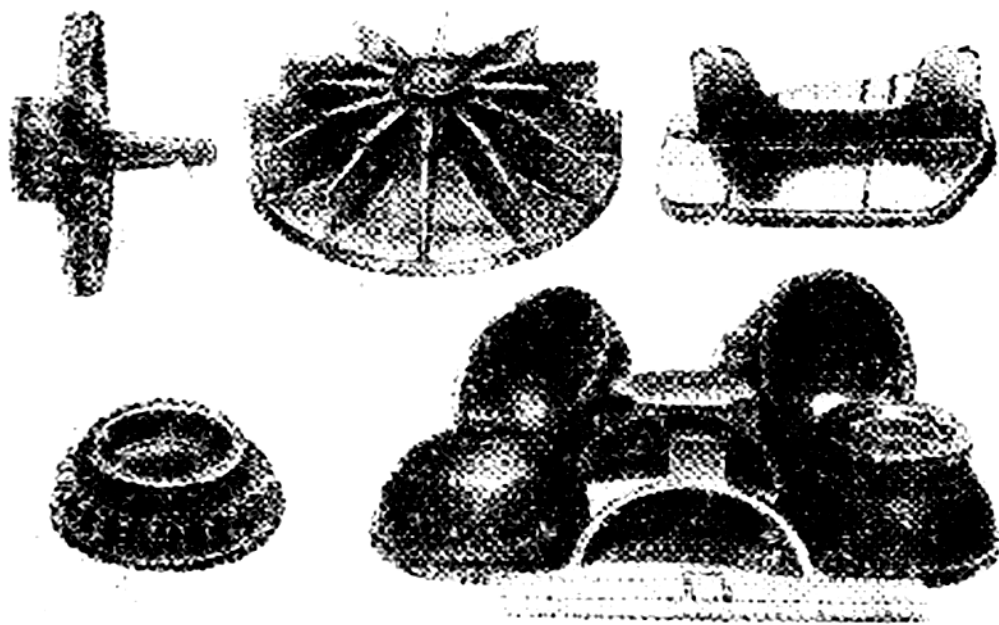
Типовые заготовки, изготовленные высокоскоростной штамповкой.
